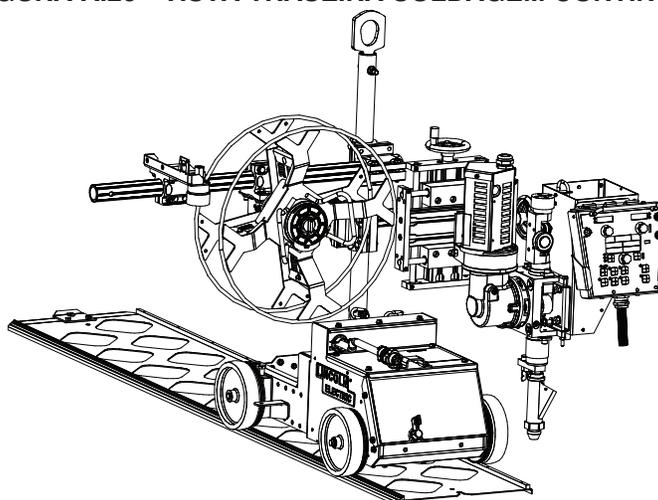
VISTA DE TOPO SOLDAGEM CONTINUA
